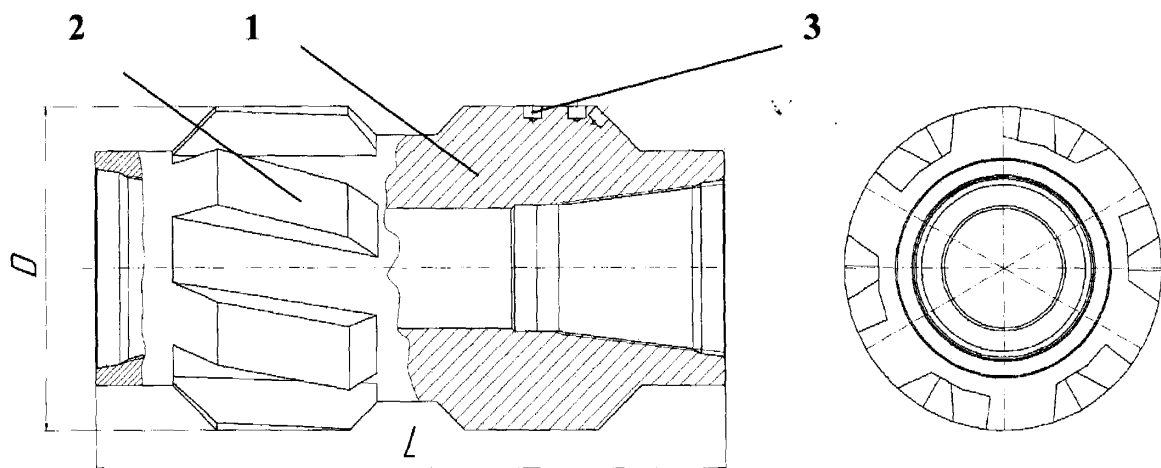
Конструктивна схема калібратора ІНМ-К-215,9 СТ.
